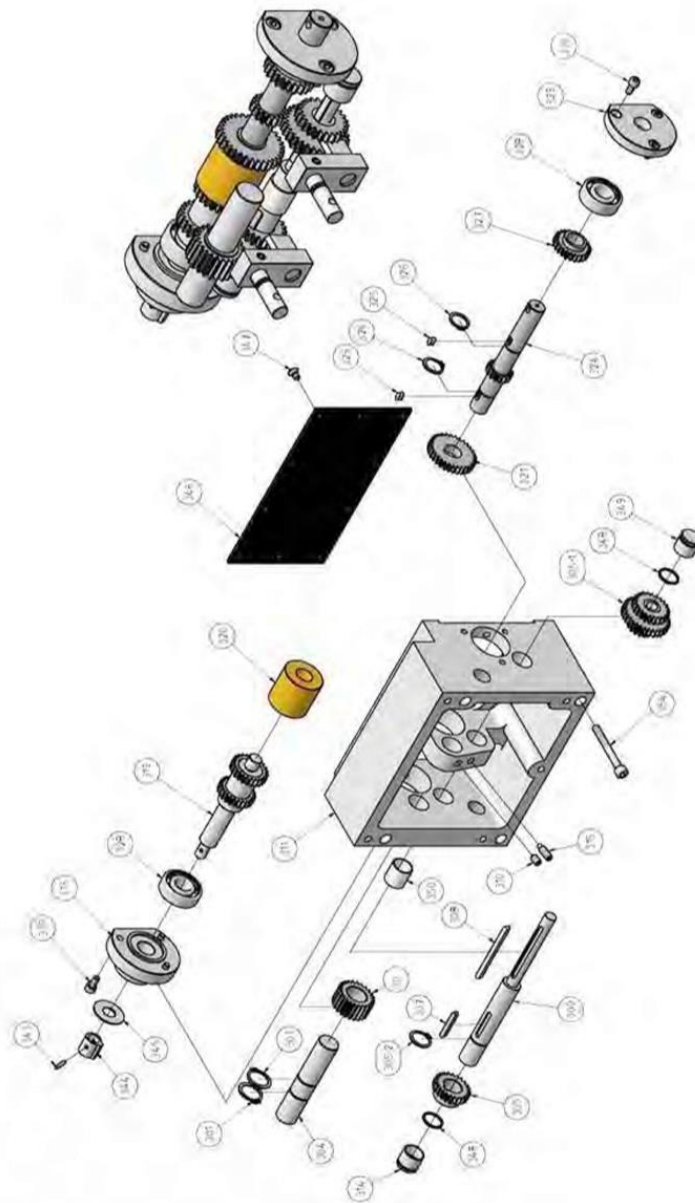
Vorschubgetriebe 2 von 2 - Engranajes de alimentación 2 de 2 - TU 2807
